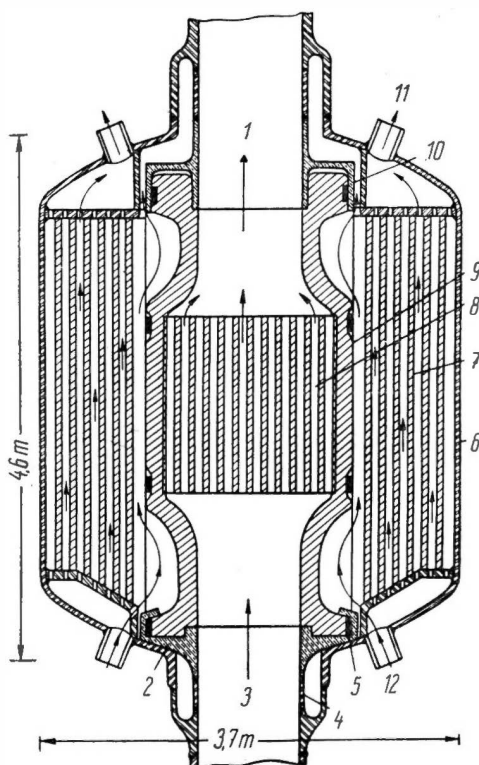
Mittelschneller produzierender Reaktor „LMFR“
